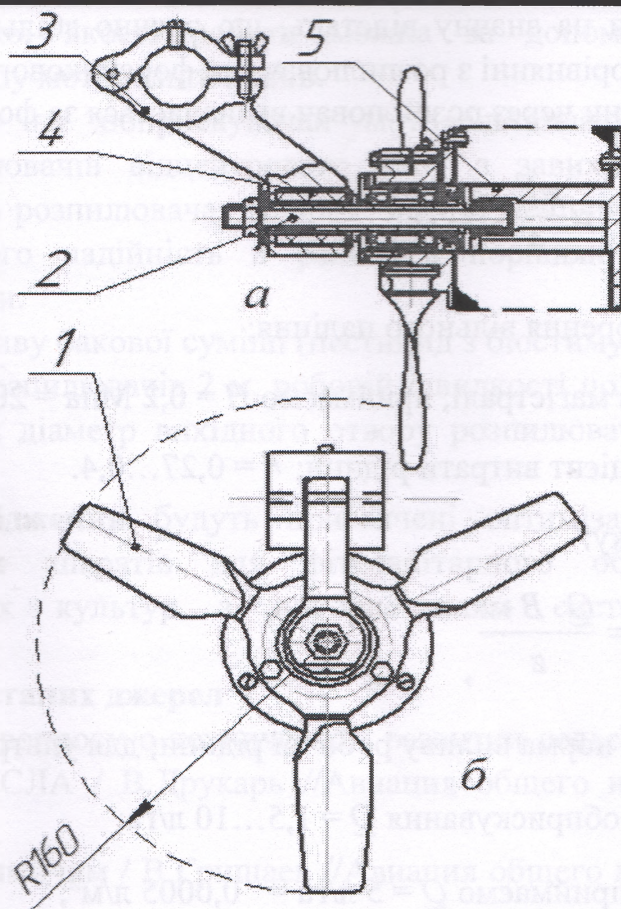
Обертовий циліндричний розпилювач: а – вид збоку;
